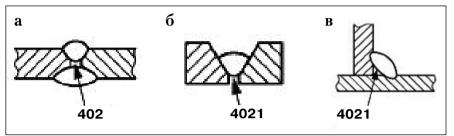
Непровар при двухсторонней сварке (а, индекс 402) и непровар корня шва при сварке встык (б, индекс 4021) и в угол (в, индекс 4021) [3, 4]
